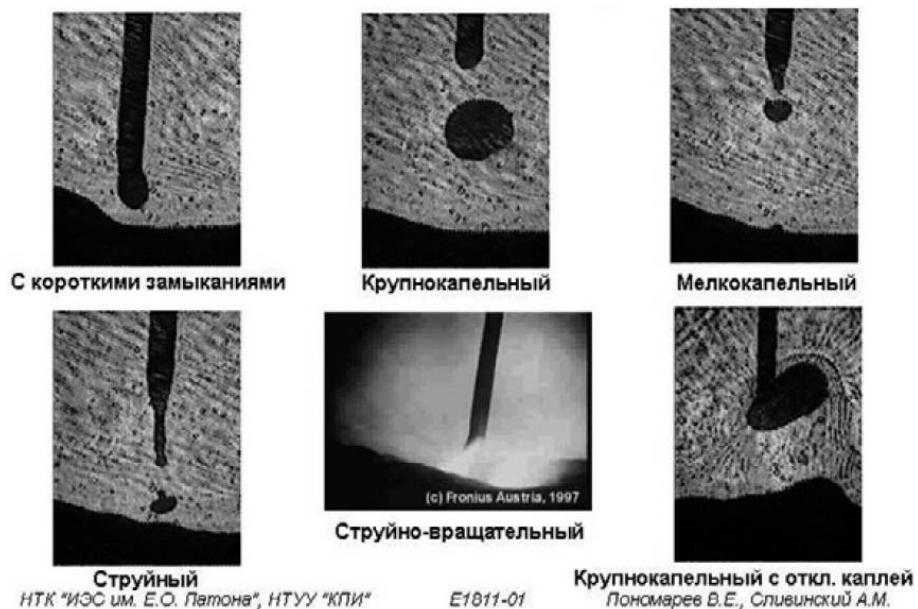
Основные типы переноса металла при механизированной сварке
